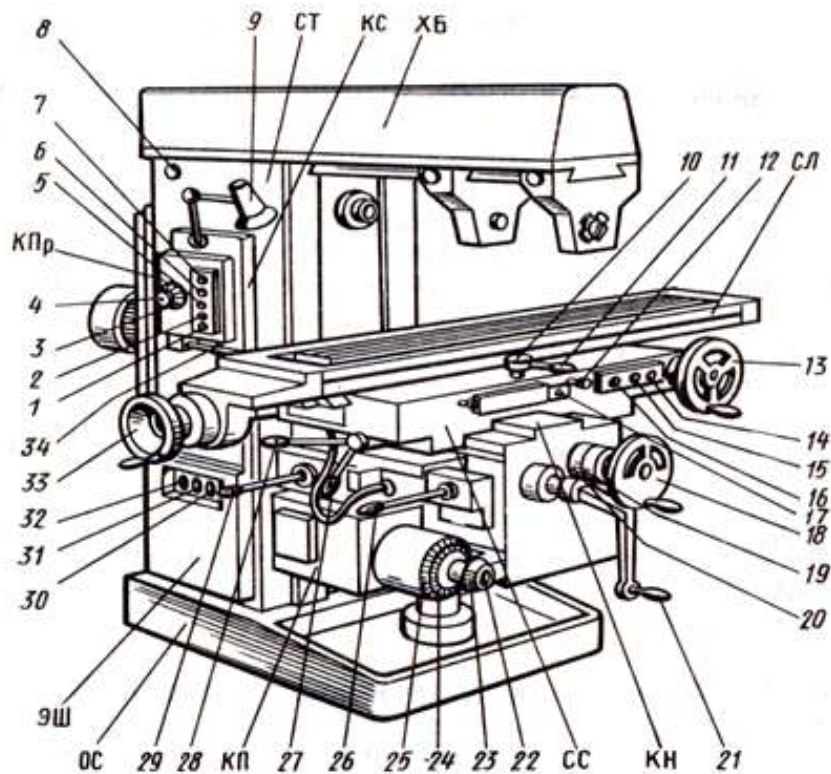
Основні частини верстата та система управління універсального горизонтально-фрезерного верстата: ОС – основа; ЕШ – електрошафа; КПр - коробка перемикання; СТ – станина; КС – коробка швидкостей ХБ – хобот із підтримуючими кронштейнами; СЛ – стіл; КН – консоль; КП – коробка подач; 1 – кнопка «Стоп» (дублююча); 2 - кнопка «Пуск шпинделя» (дублююча); 3 – стрілка-показчик швидкостей шпинделя; 4 – показчик швидкостей шпинделя; 5 – кнопка «Швидко стоп» (дублююча); 6 - кнопка "Імпульс шпинделя"; 7 – перемикач освітлення; 8 – шестигранник для переміщення хобота; 9 – арматура освітлення; 10 - зірочка механізму автоматичного циклу; 11 – рукоятка включення поздовжніх переміщень столу; 12 – затискачі столу; 13 – маховичок ручного поздовжнього переміщення столу; 14 – кнопка «Швидко стоп»; 15 - кнопка "Пуск шпинделя"; 16 – кнопка «Стоп»; 17 – перемикач ручного або автоматичного керування поздовжнім переміщенням столу; 18 – маховичок ручних поперечних переміщень столу; 19 – лімба механізму поперечних переміщень столу; 20 - кільце-ноніус; 21 – рукоятка ручного вертикального переміщення столу; 22 - кнопка фіксації грибка перемикання подач; 23 - грибок перемикання подач; 24 - показчик подач столу; 25 - стрілка-показчик подач столу; 26 – рукоятка включення поперечної та вертикальної подач столу; 27 - затискач салазок на напрямних консолі; 28 – рукоятка включення поздовжніх переміщень столу (дублююча); 29 – рукоятка включення поперечної та вертикальної подач столу (дублююча); 30 – перемикач напряму обертання шпинделя «ліворуч – праворуч»; 31 – перемикач насоса охолодження; 32 – перемикач введення «включено – вимкнено»; 33 – маховичок ручного поздовжнього переміщення столу (дублюючий); 34 – рукоятка перемикання швидкостей шпинделя.
